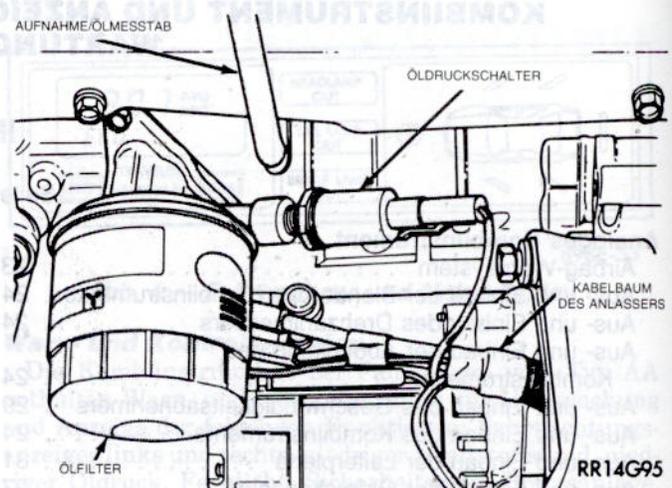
Öldruckschalter (3,0-ltr.-Motor)
